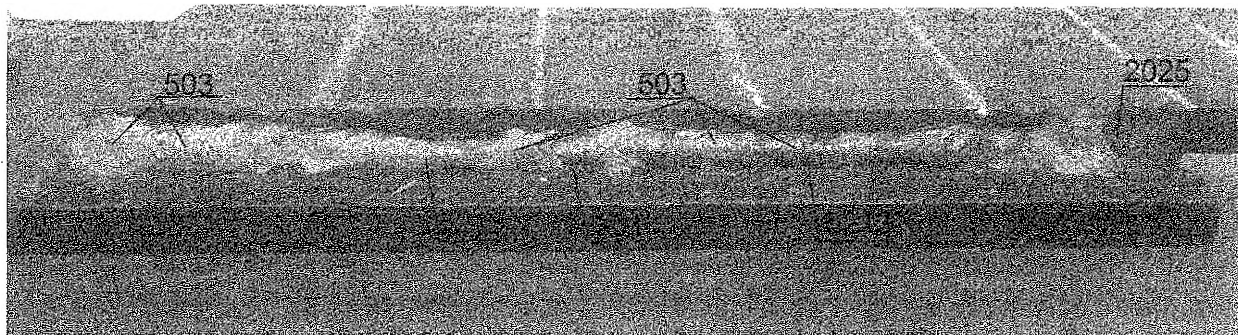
Дефекты углового сварного шва со стороны 1
